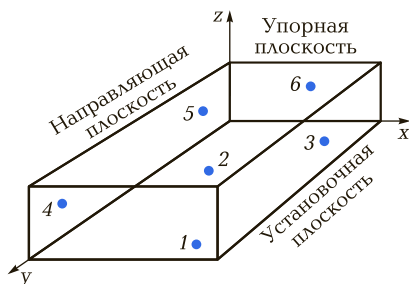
Трехмерное базирование детали прямоугольной призматической формы:
